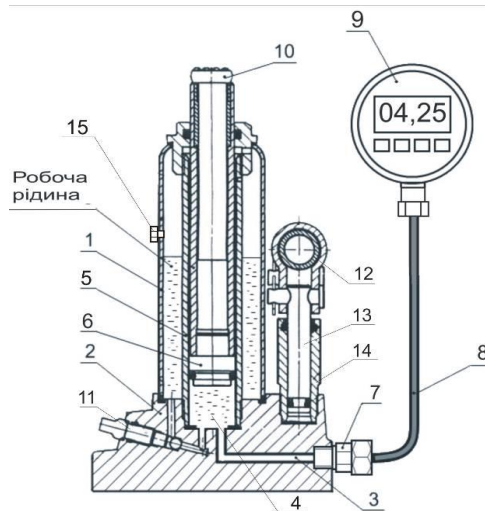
Прилад ваговимірювальний гідравлічний ПВГ-5Е
